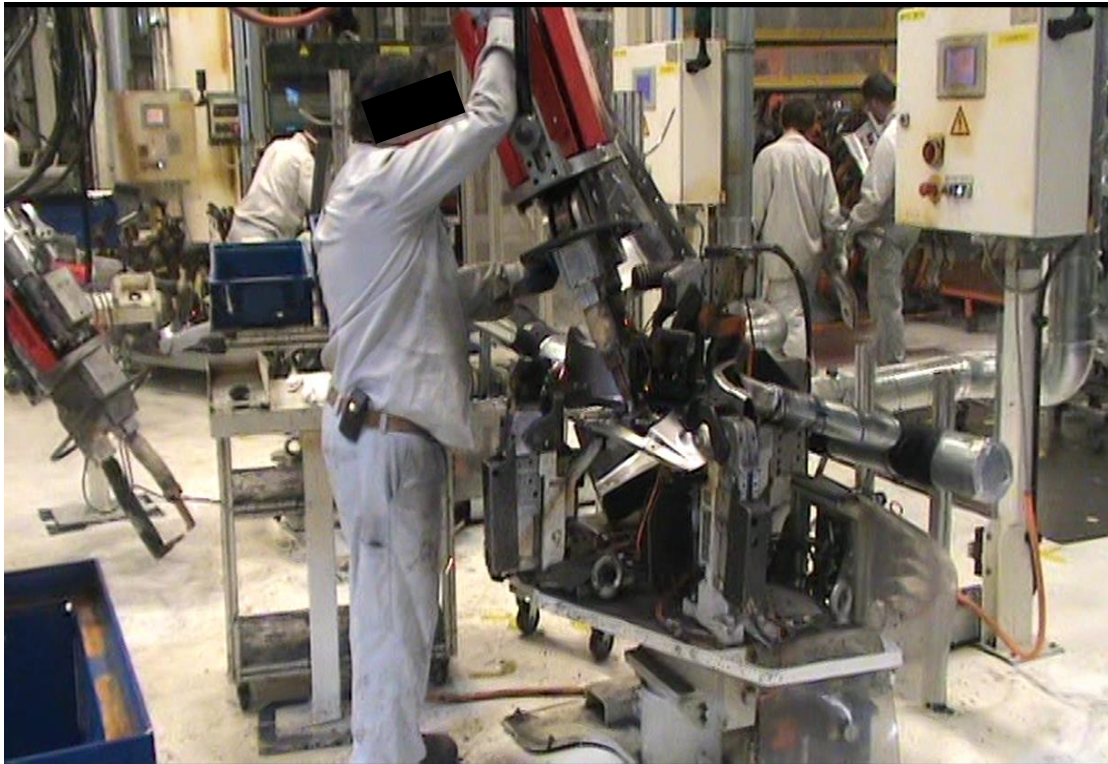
Situação H Manipulação da pistola de soldadura
